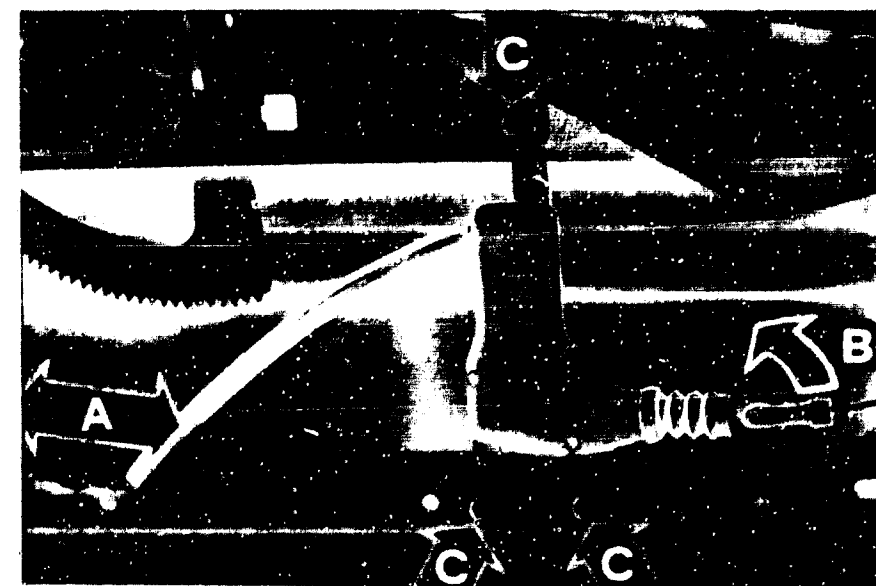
Beim Ausbau des Motors für die Zentraltürverriegelung sind der Stecker (A) zu trennen, die Sicherung vom Fernbetätigungsgestänge (B) abzunehmen und die Befestigungsschrauben (C) zu lösen.
